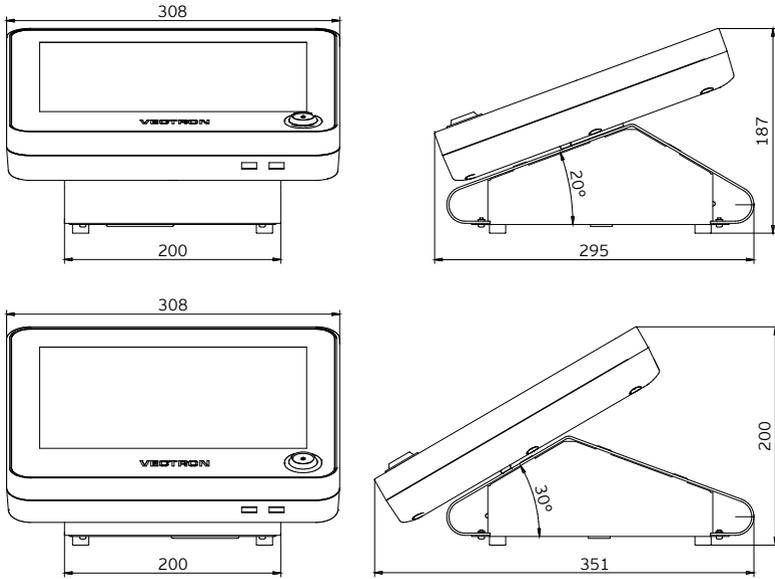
POS Touch 12 Dimensions pied S500 inclu (en mm)
